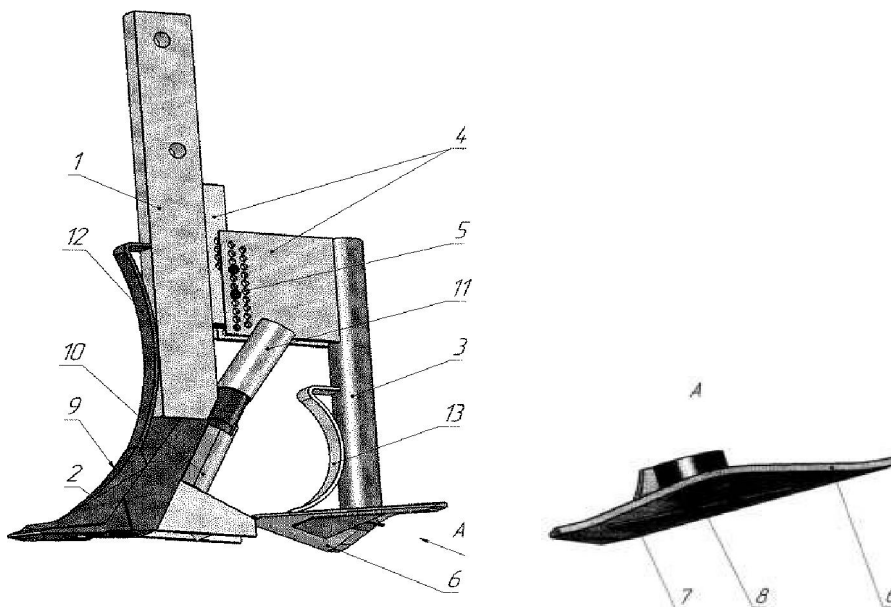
Робочий орган сівалки: 1 - стійка; 2 - розпушувач; 3 - трубчаста стійка; 4 - регулювальні пластини; 5 - кріплення; 6 - стрільчата лапа; 7 - пластина; 8 - розподільник насіння; 9 - ріжуча поверхня; 10 - труба; 11 - коліно; 12 і 13 - напрямні
